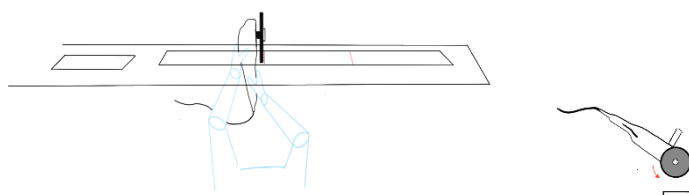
Corte no lado exterior do corte + Rotação correta do disco para efetuar o corte
